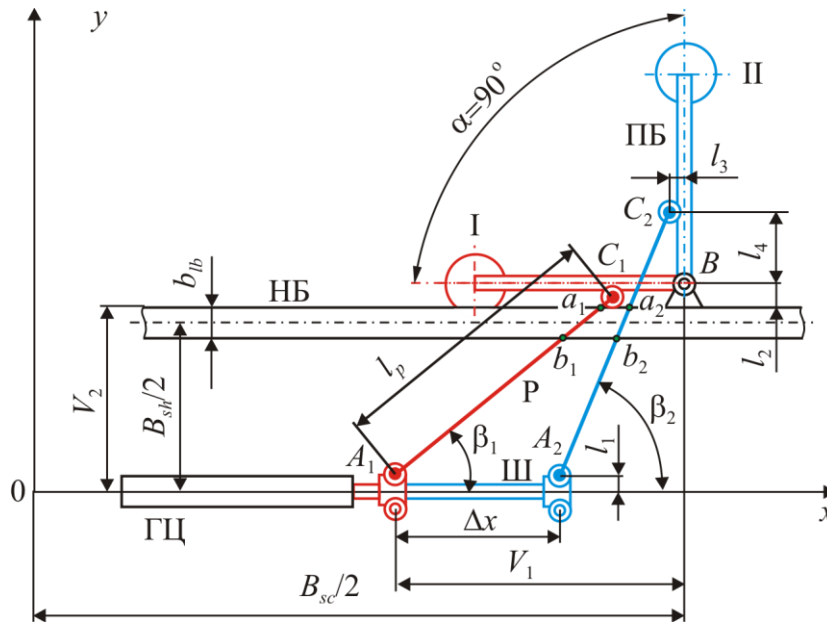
Кинематическая схема установки выносной опоры из транспортного положения I в рабочее положение II (ГЦ – гидроцилиндр; НБ – надрамная балка; ПБ – поворотная балка; Р – рычаг; Ш – шток)
